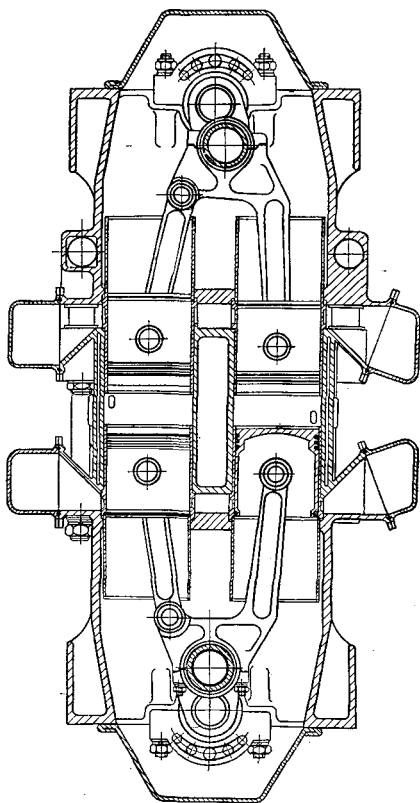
Схема двигателя с параллельными цилиндрами и шатунами усложненной конструкции
